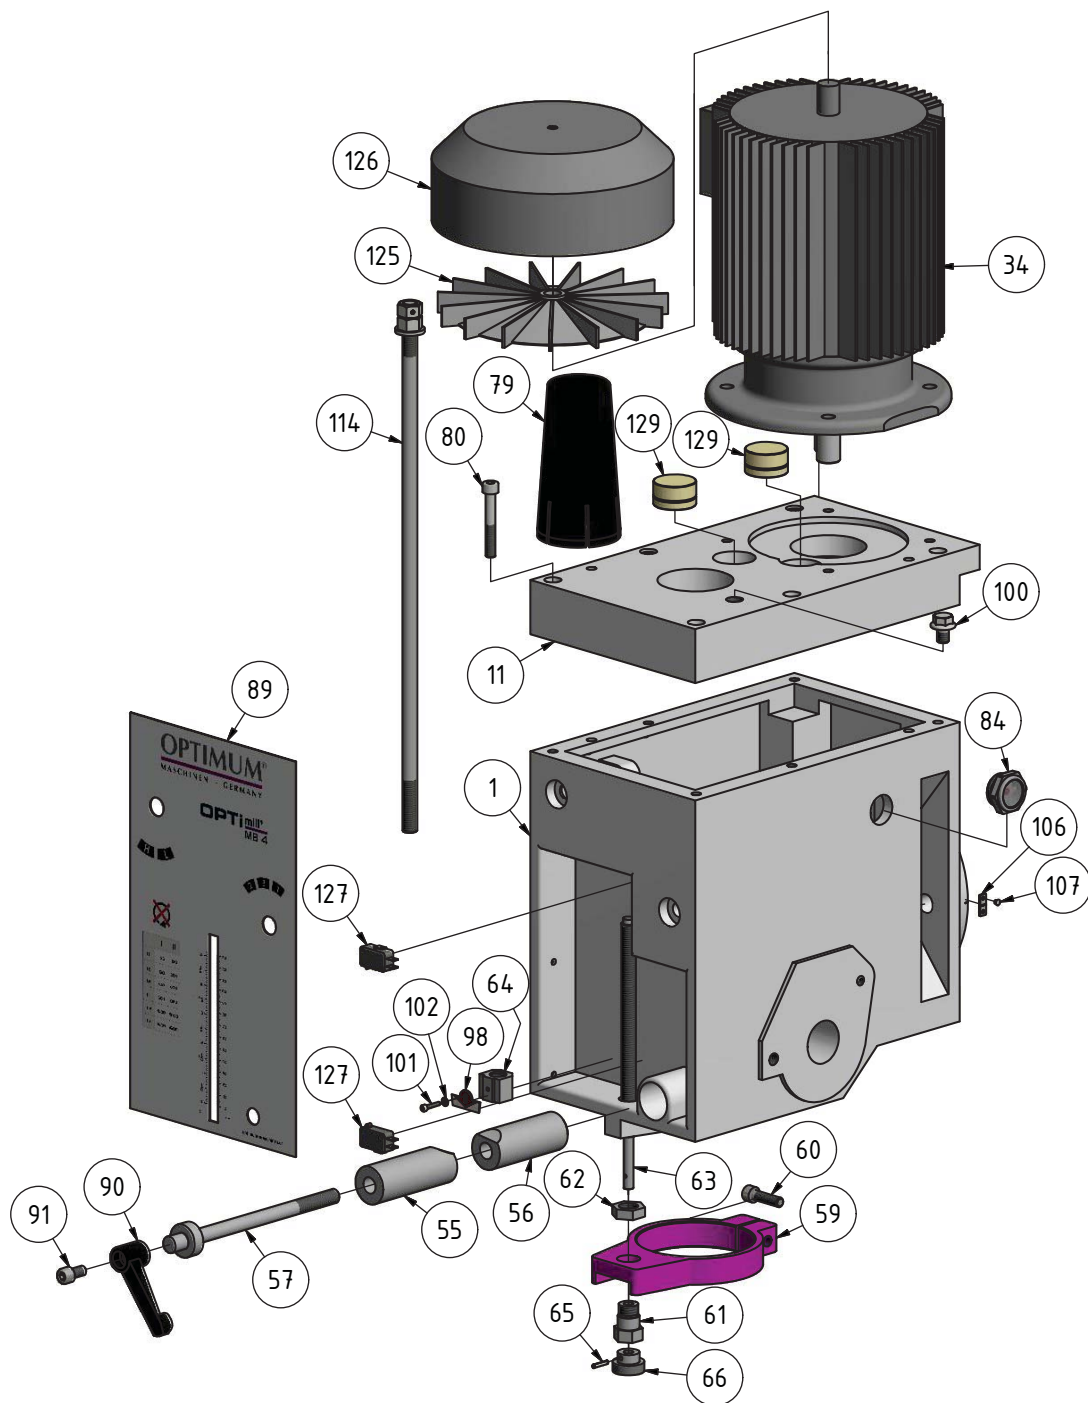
Fräskopf 6 von 6 - Milling head 6 von 6
